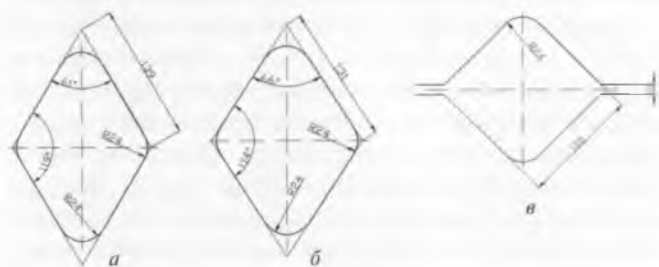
Вид заготовки (а, б) и инструмента (в) для моделирования прокатки ромбической заготовки в квадратном калибре
